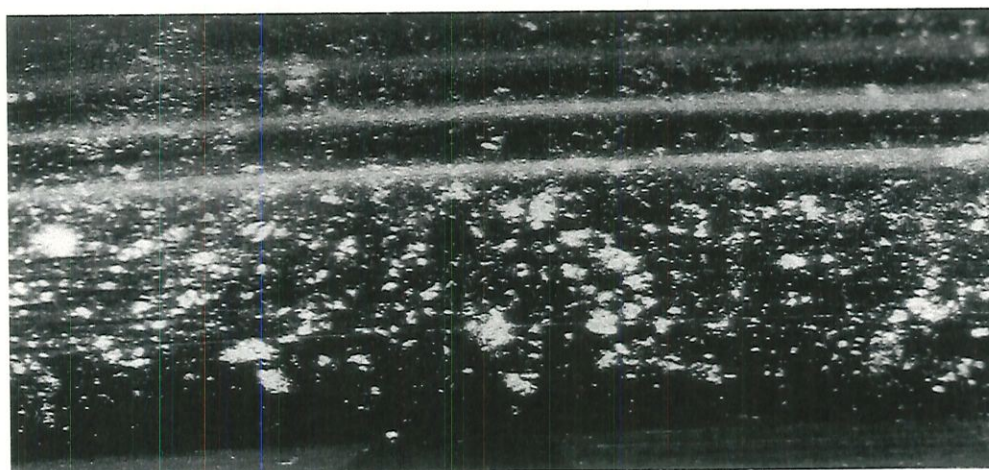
Falha na pista externa tipo “cavitações” (IZHPZ 6204).
